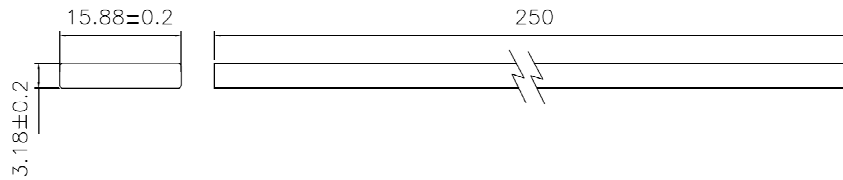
Geometría de platina usada para probetas de ensayo. (Medidas en mm).
